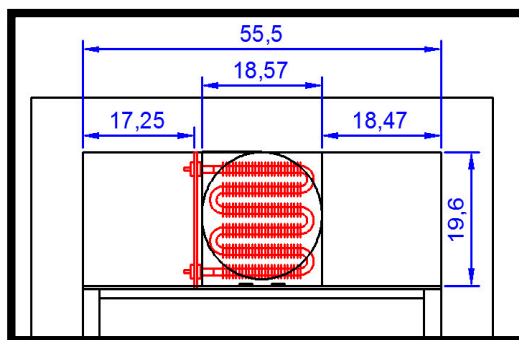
Vista frontal de las medidas para la colocación del elemento calefactor. Elaboración: Los autores
